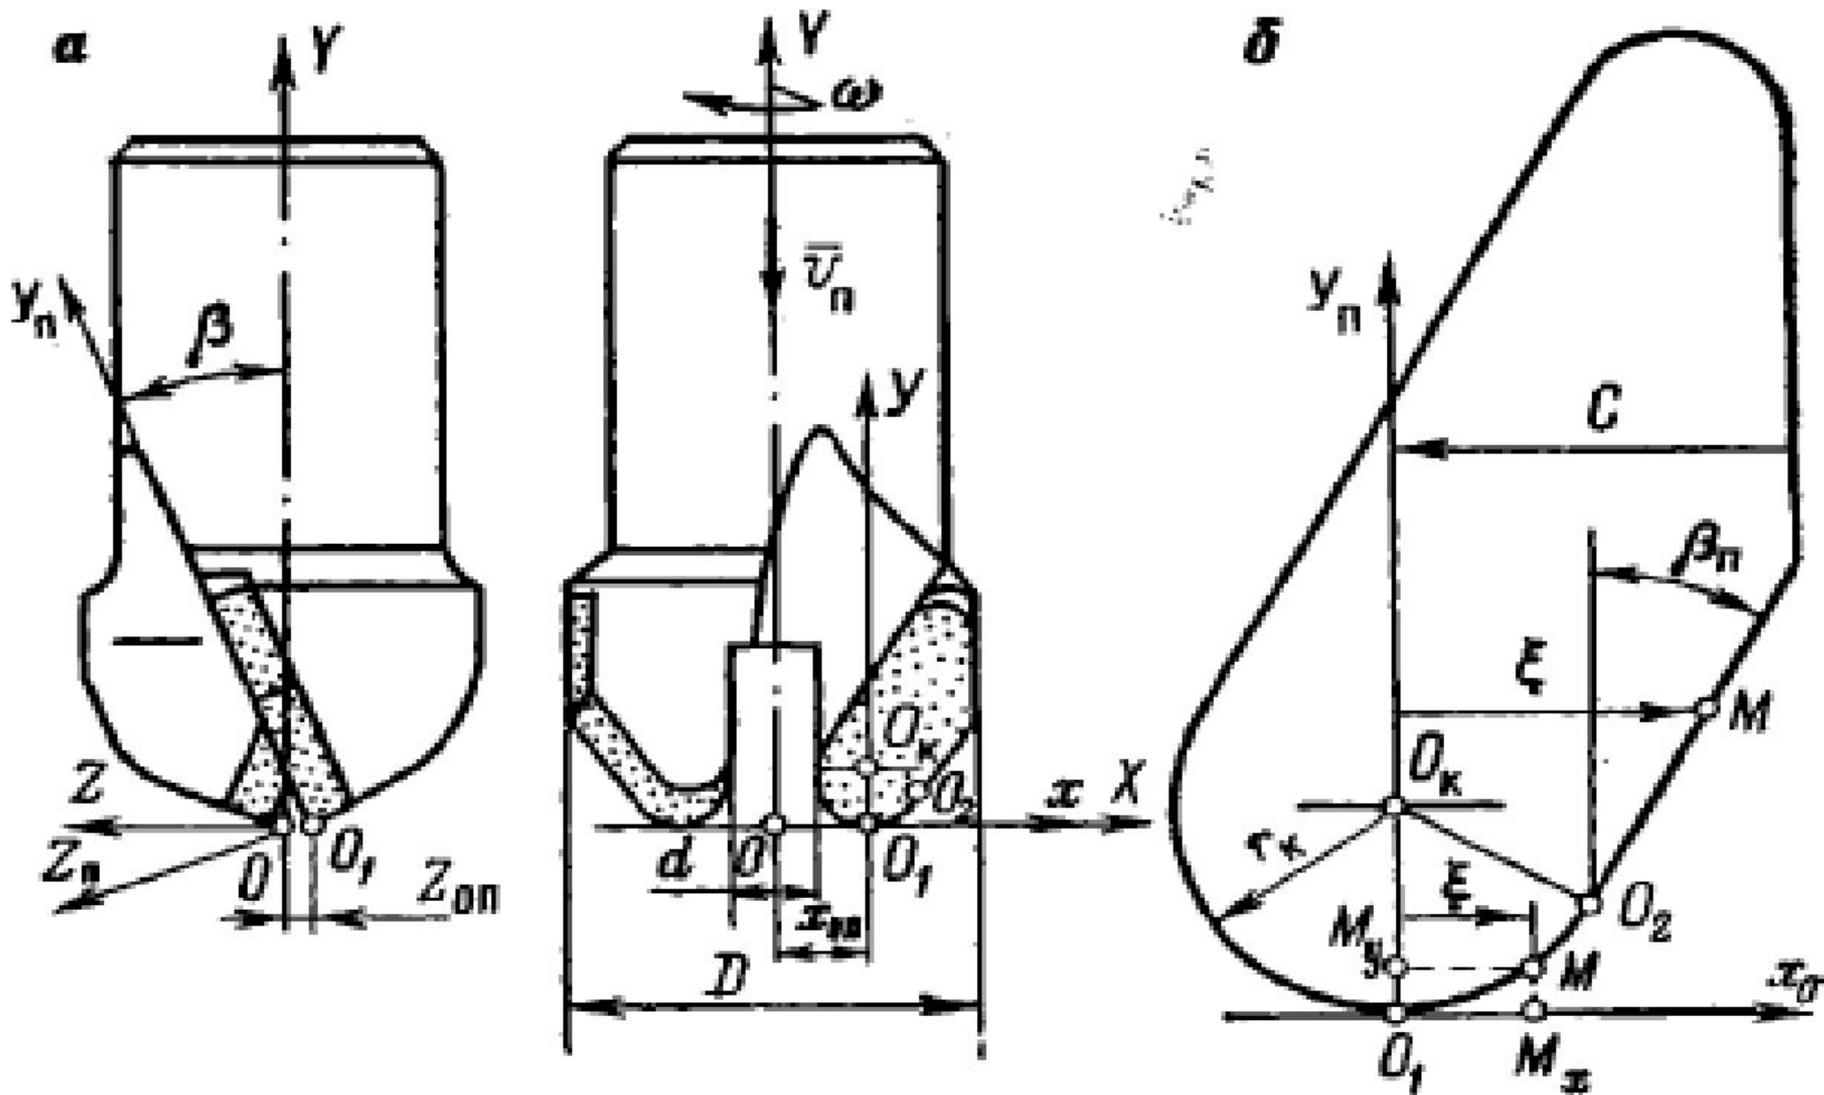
Общий вид (а) и конструктивные параметры (б) резца РП – 42 и армирующей пластинки
